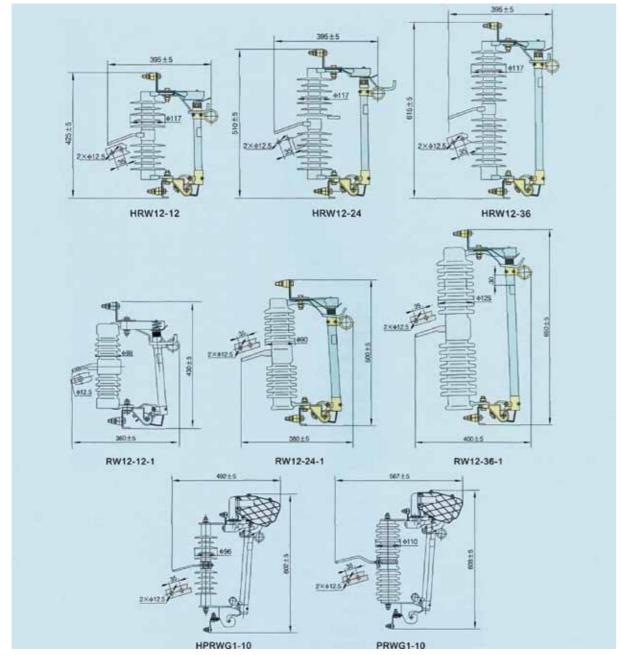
Внешний вид и размеры откидывающегося плавкого предохранителя
